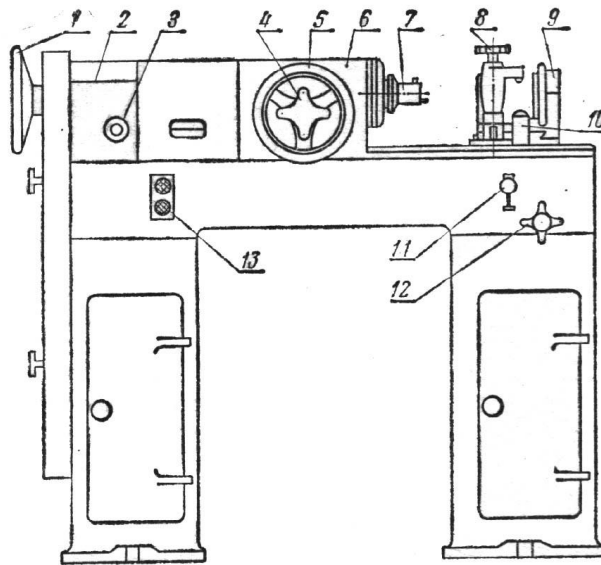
Горизонтально-розточувальний верстат УРБ-ВП-М: 1 – маховичок для провертання шпинделя; 2 – коробка передач; 3 – вказівник рівня масла; 4 – гайка включення автоматичної подачі; 5 – маховичок пересування шпинделя; 6 – стояк шпинделя; 7 – різцева головка; 8 – притискний стояк; 9 – каретка з призмами; 10 – нижній подвижний упор; 11 – рукоятка кріплення упору; 12 – рукоятка механізму піднімання упору; 13 – кнопки «Пуск» і «Стоп» верстату.
